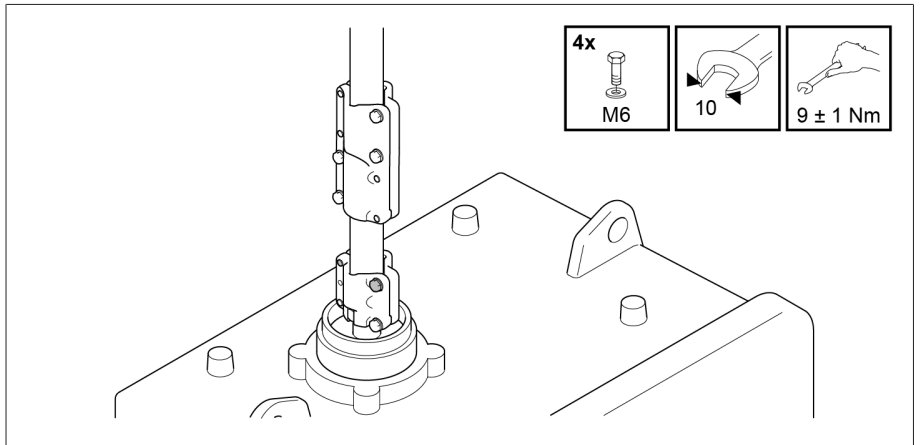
Fixer le tube carré sur le mécanisme d'entraînement
